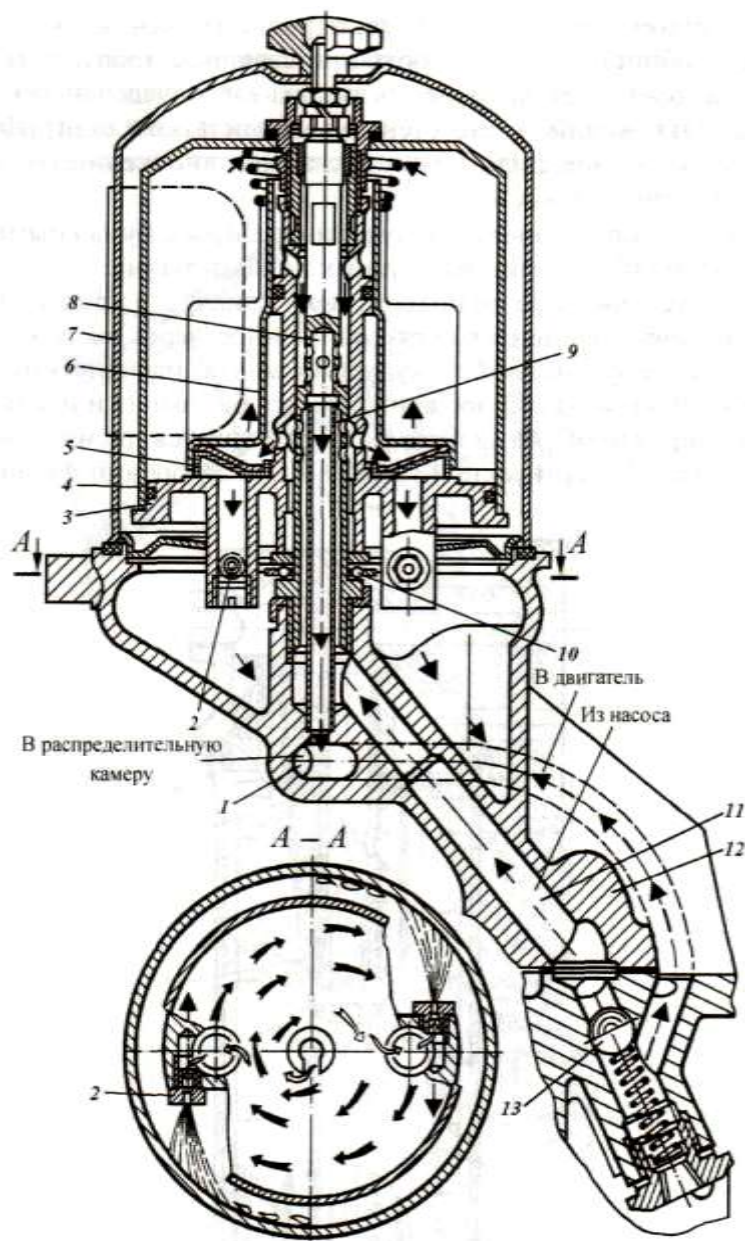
Центробежный фильтр двигателя ЗИЛ-4314:
